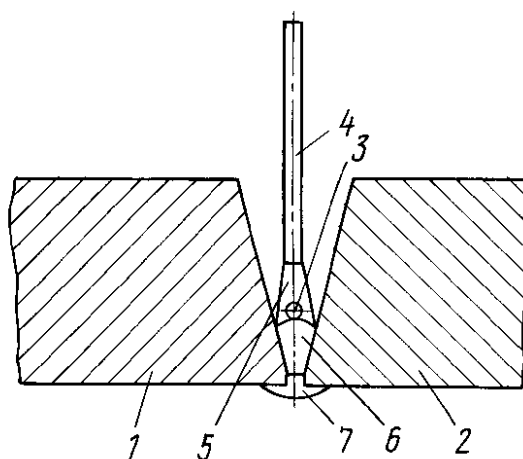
Схема выполнения сварки с дополнительной присадочной проволокой
